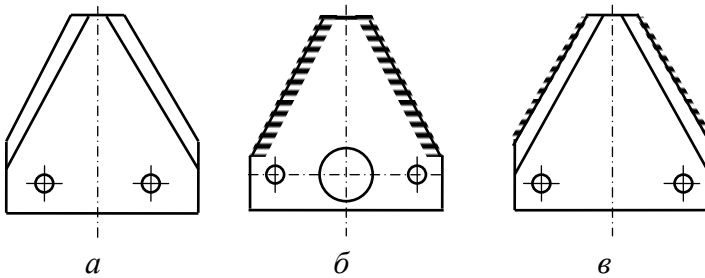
Основные варианты исполнения сегментов сегментно-пальцевого режущего аппарата: а – с гладкой режущей кромкой; б – с рифленой режущей кромкой; в – с режущей кромкой с зубчиками.
